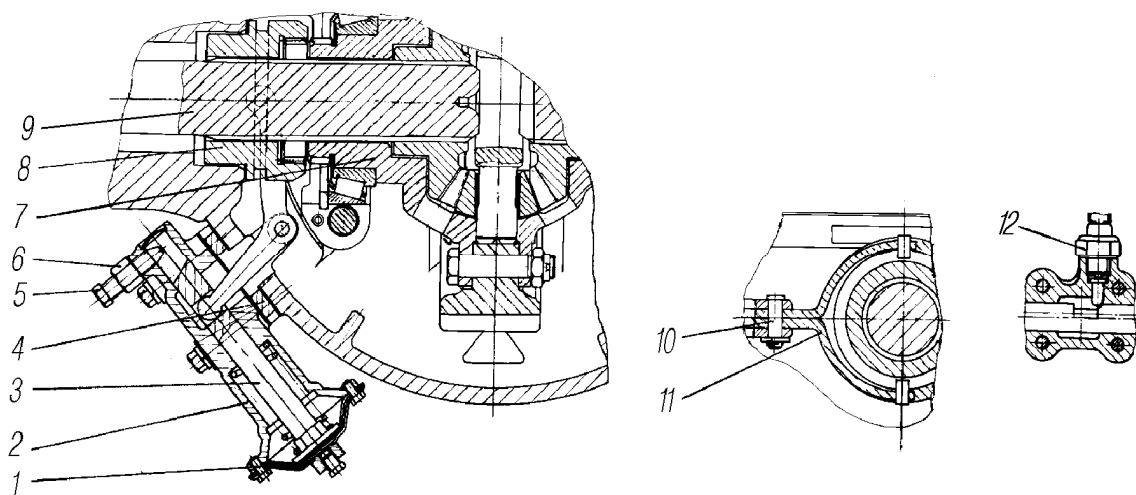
Дифференциал межколесный заднего моста с принудительной блокировкой: 1- диафрагма; 2- корпус механизма включения блокировки; 3- шток; 4- кронштейн; 5- ограничитель; 6- гайка; 7- чашка дифференциала; 8- муфта; 9- полуось; 10- палец; 11- вилка; 12- выключатель ВК403А
